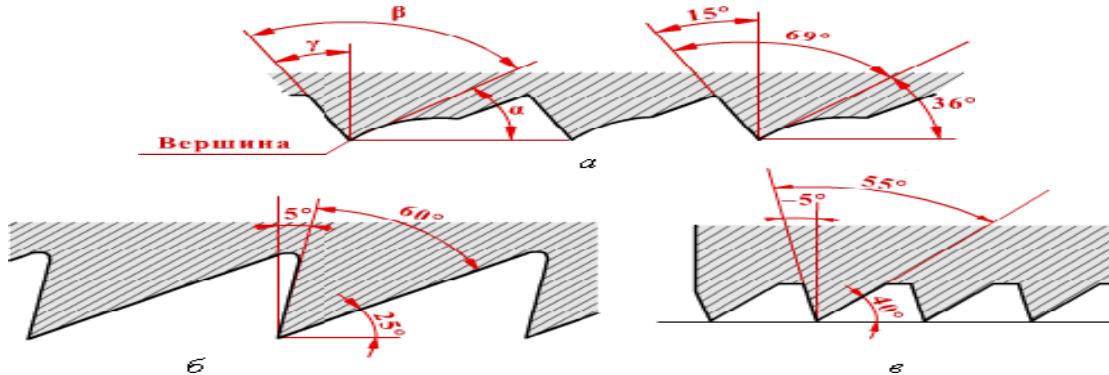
Зубці напилка: *а*—насічені; *б*—дістали фрезеруванням або шліфуванням; *в* — дістали протягуванням
